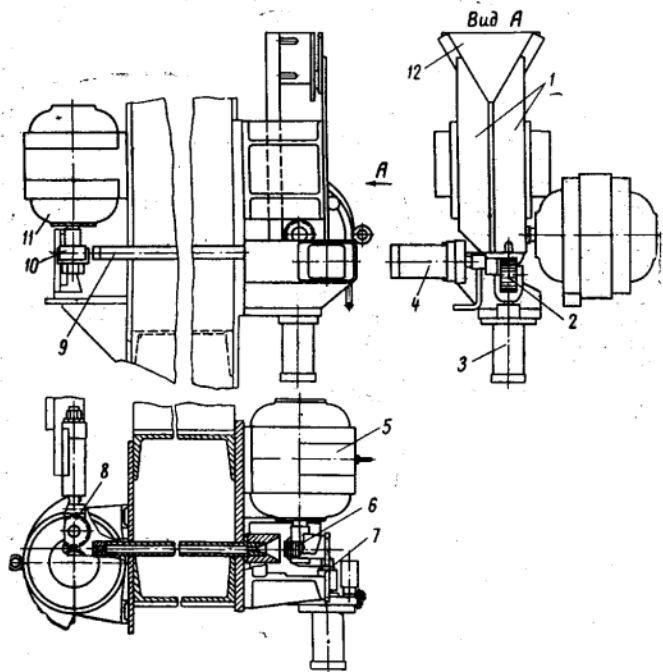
Многоэлектродная машина АТМС-14х74-7 для точечной сварки сеток шириной до 3800 мм (вид сбоку)
